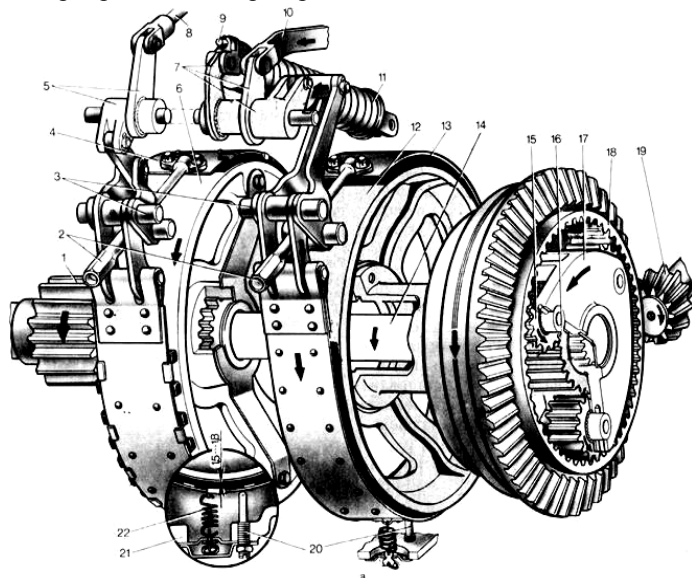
Устройство планетарного механизма поворота (левый): 1 - ведущая шестерня конечной передачи; 2 – регулировочные гайки; 3 - пальцы; 4 — тормозная лента остановочного тормоза; 5 - рычаги остановочного тормоза; 6 - шкив остановочного тормоза; 7 - рычаги тормоза солнечной шестерни; 8 - тяга управления остановочным тормозом; 9 - шток-указатель регулировки тормоза солнечной шестерни; 10 - тяга управления тормозом солнечной шестерни; 11 и 22 - пружины; 12 - шкив тормоза солнечной шестерни; 13 - тормозная лента солнечной шестерни; 14 - полуось (вал); 15 - сателлит; 16 - солнечная шестерня; 17 - водило; 18 - коронная шестерня; 19 - ведущая шестерня главной передачи; 20 - регулировочные винты; 21 - корпус заднего моста
